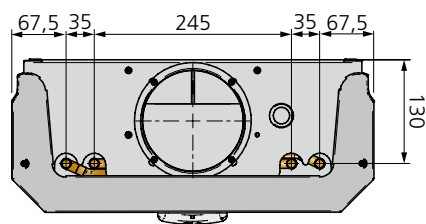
Dimensions ADRIATIC AWC Prisma, vue arrière du raccordement hydraulique
